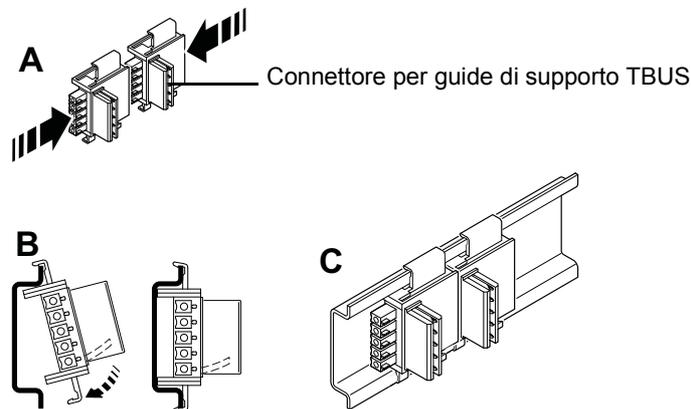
Montaggio di connettori per guide di supporto TBUS
